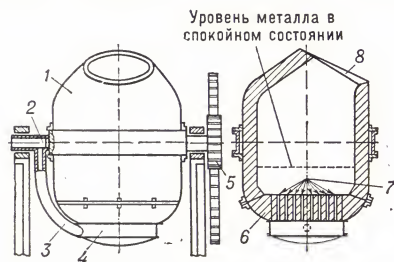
Бессемеровский конвертер: 1 — корпус; 2 — пустотелая цапфа; 3 — патрубок; 4 — воздушная коробка; 5 — редуктор; 6 — дутьевая фурма; 7 — фурмы; 8 — горловина.
